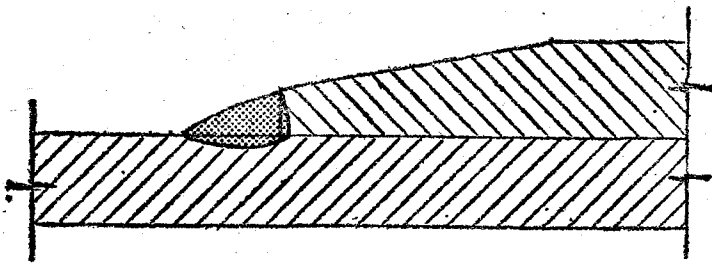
Soldadura frontal en el extremo de una platabanda traccionada
